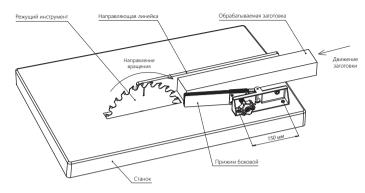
A Установка прижима бокового на станок с вращением инструмента по часовой стрелке
